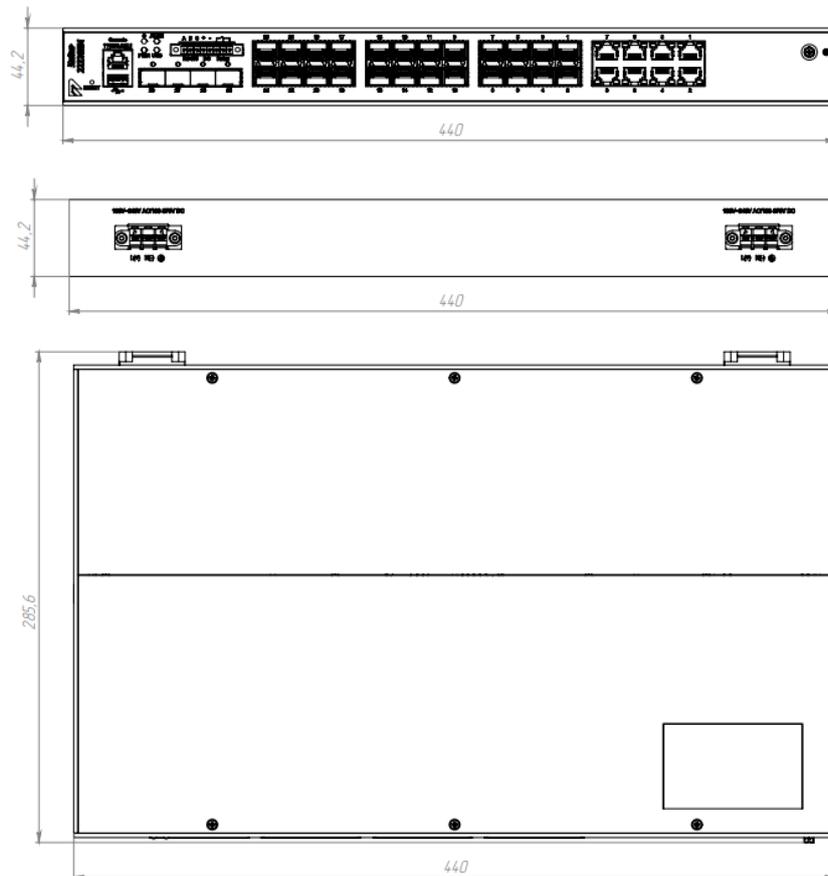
Габаритные и установочные размеры аппарата ИнЗер®-2222GEM (БЛПА.465255.132-00.01)
